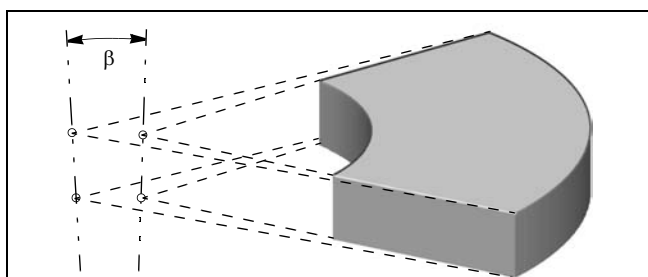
Модель детали Ω_3 с непараллельными осями внешней и внутренней цилиндрических поверхностей
